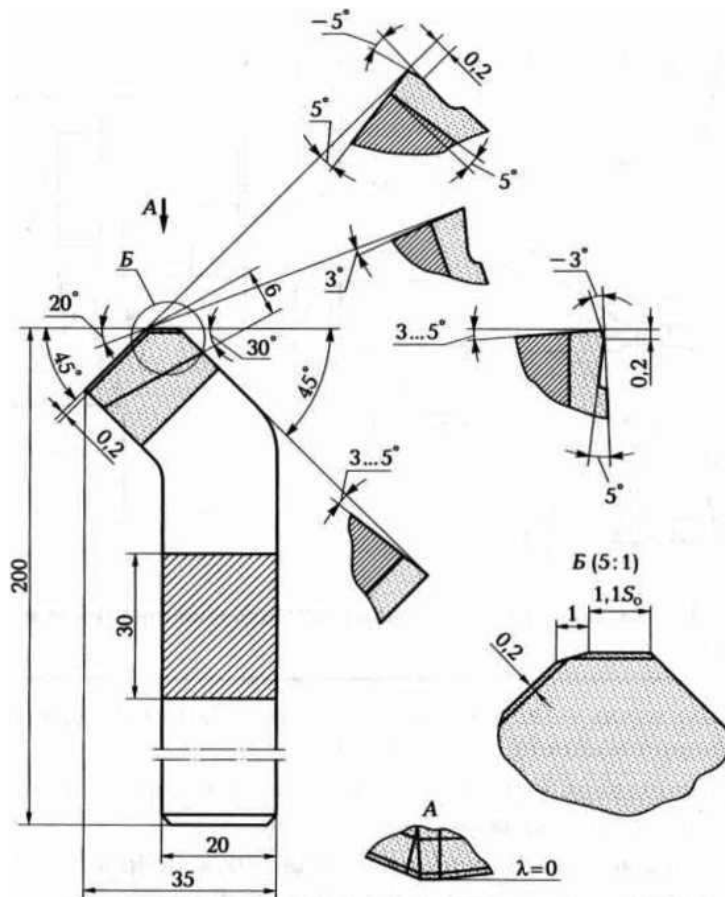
Проходной отогнутый резец конструкции Колосова
